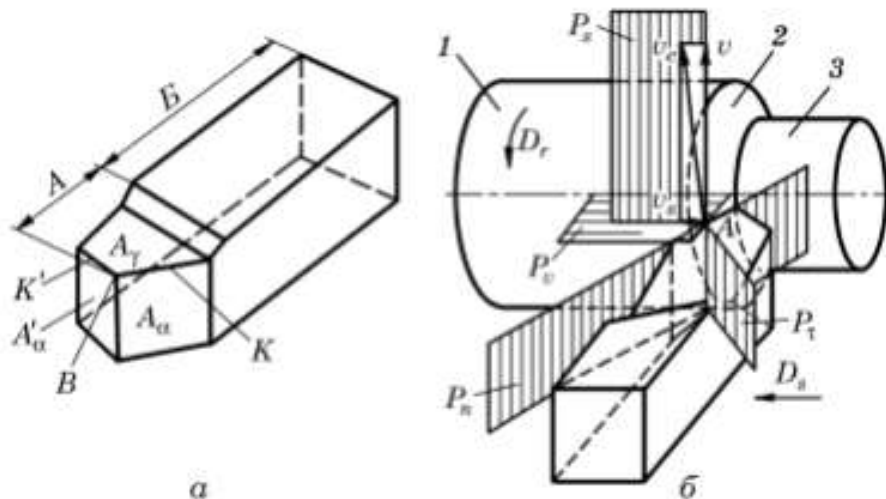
Елементи проходного токарного різця (а), поверхні заготовки та координатні площини (б)
